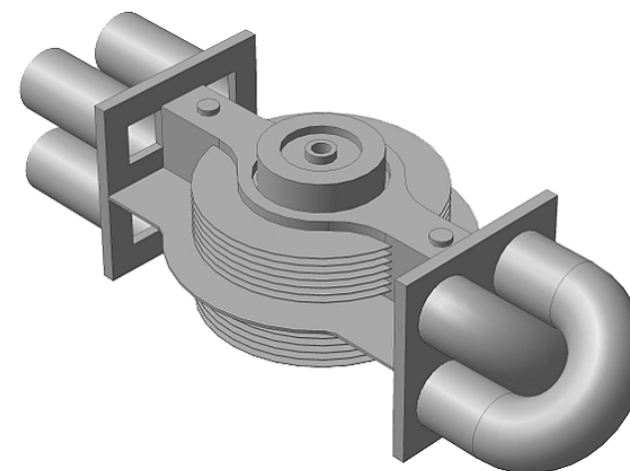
Общий вид двухступенчатого однороторного дискового вентилятора-регенератора.
